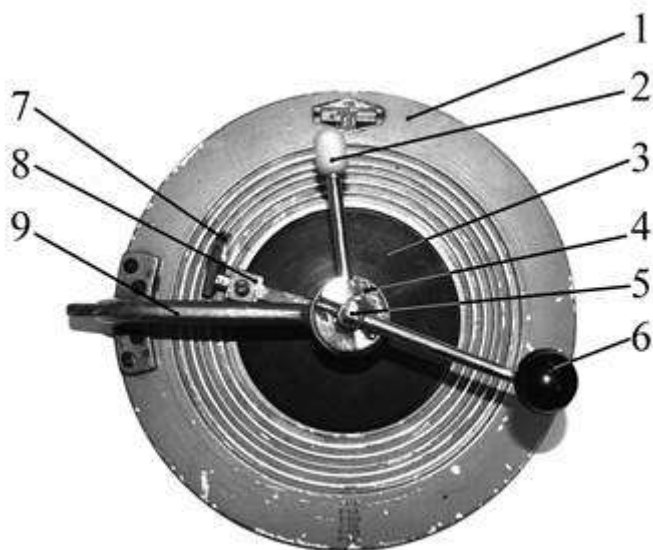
Приспособление ТММ-31А для изготовления бумажных заготовок
